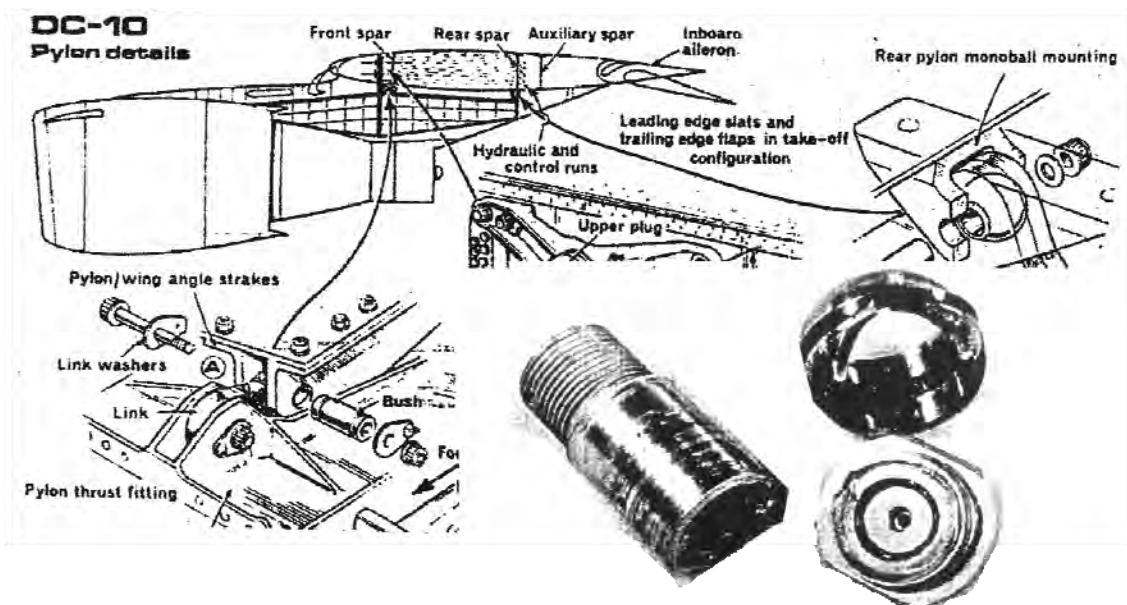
Усталостное разрушение стыкающейся детали и сферического вкладыша узла навески двигателя самолета ДС-10
